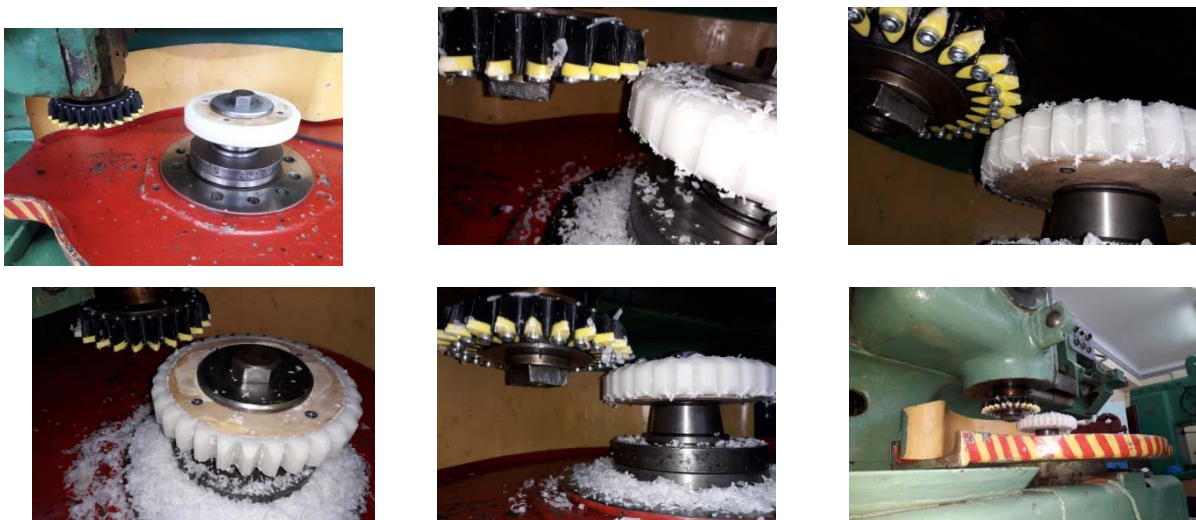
Процесс нарезания зубчатого колеса на станке 5М14
